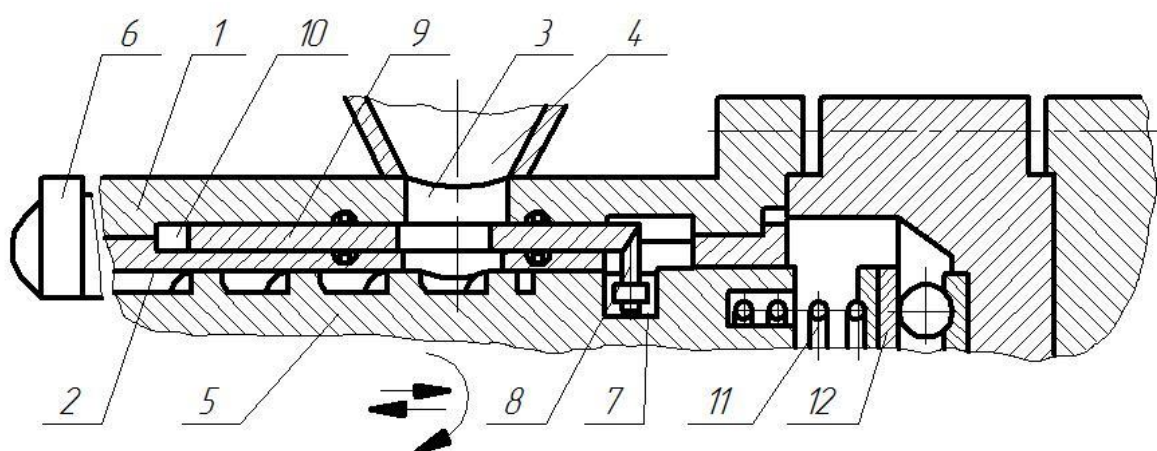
Черв'ячний екструдер для переробки полімерних матеріалів [22].
